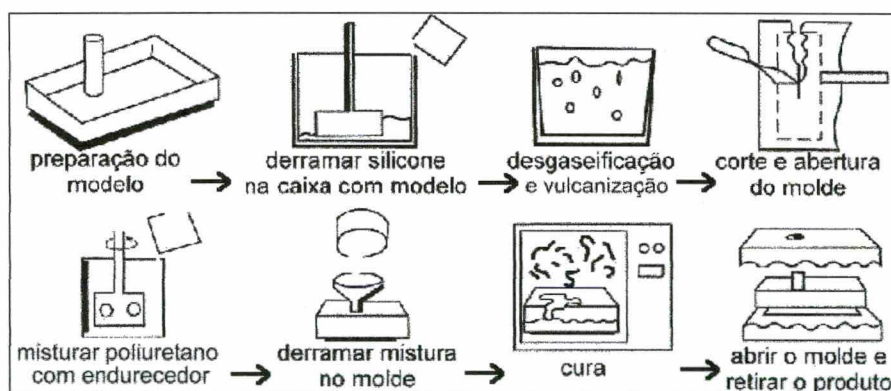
Etapas para a fabricação de peças com uso de moldes de silicone
